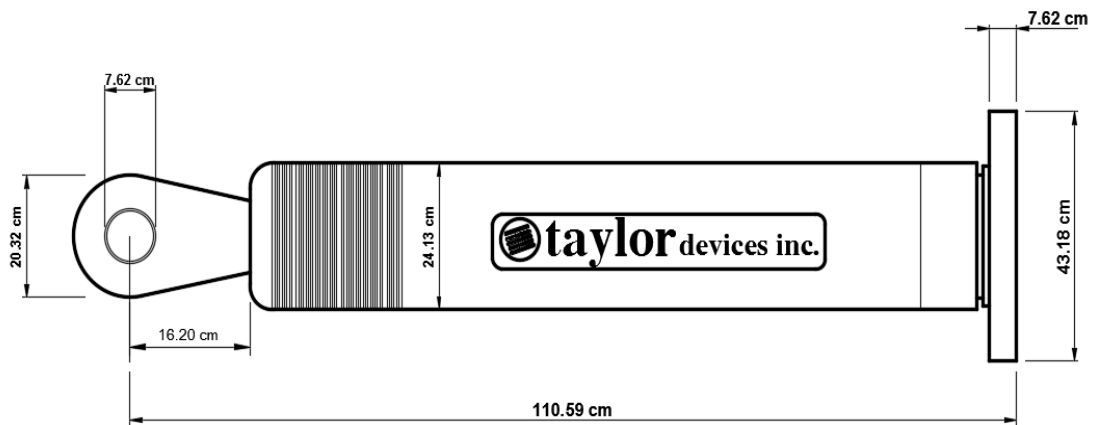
Dimensiones de disipador de 330 KIP (Fuente propia)
